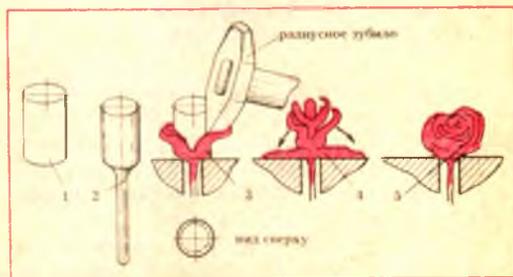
Изготовление цельнокованной розы: 1 — заготовка; 2 — оттяжка стержня; 3 — надрубка лепестков; 4 — расковка лепестков и их формовка; 5 — сформованный цветок
